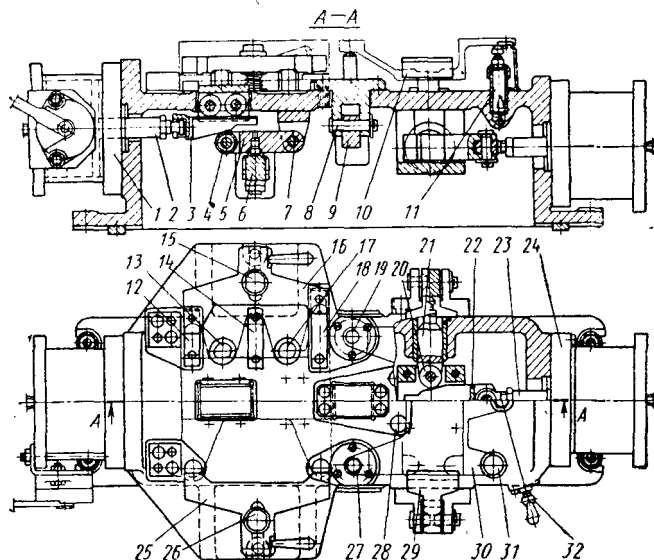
Многоместное фрезерное приспособление с клиновым усилителем зажима и дополнительными опорами
